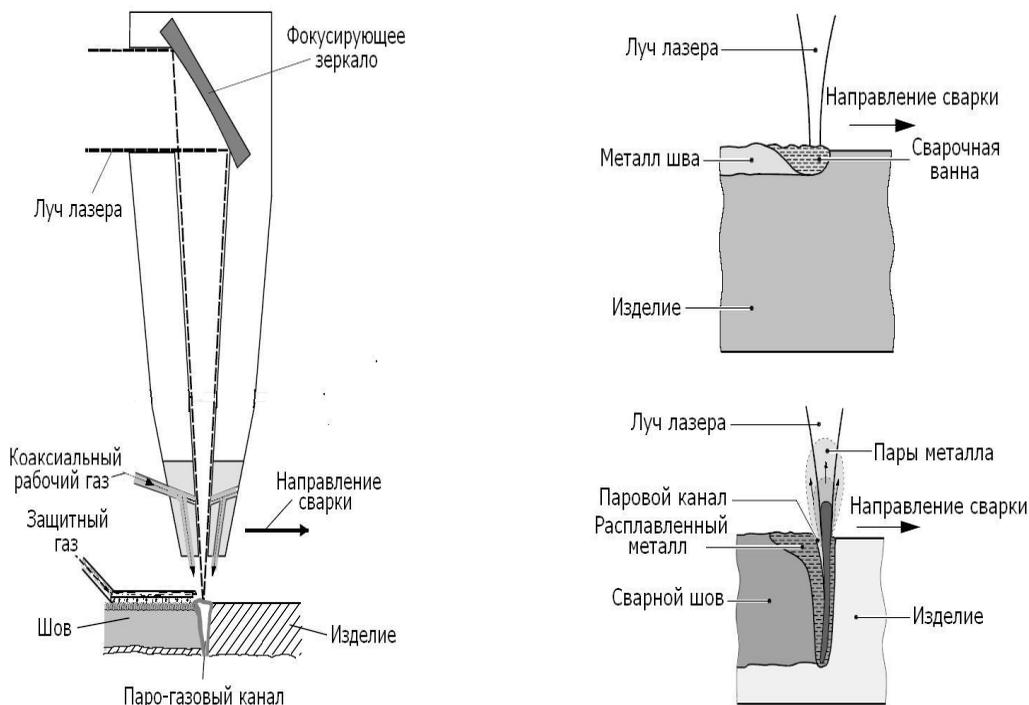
Схемы лазерной сварки: а – общая схема сварки; б – проплавление при плотности энергии менее 10^6 Вт/см²; в – проплавление при плотности энергии более 10^6 Вт/см².
